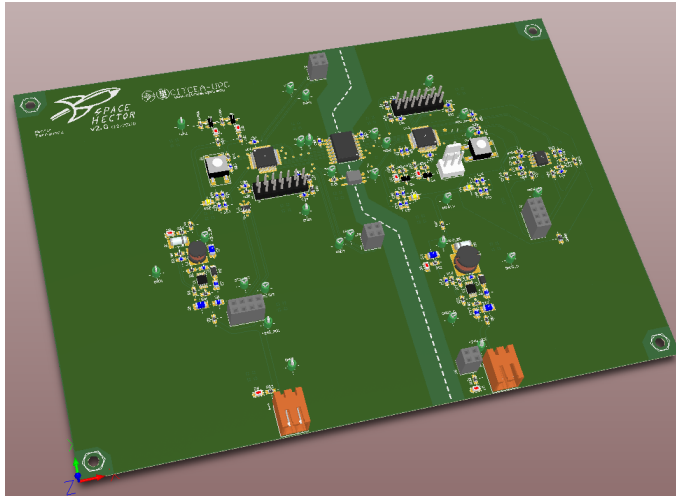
Dibuix 3D de la PCB *BlackOut*.
